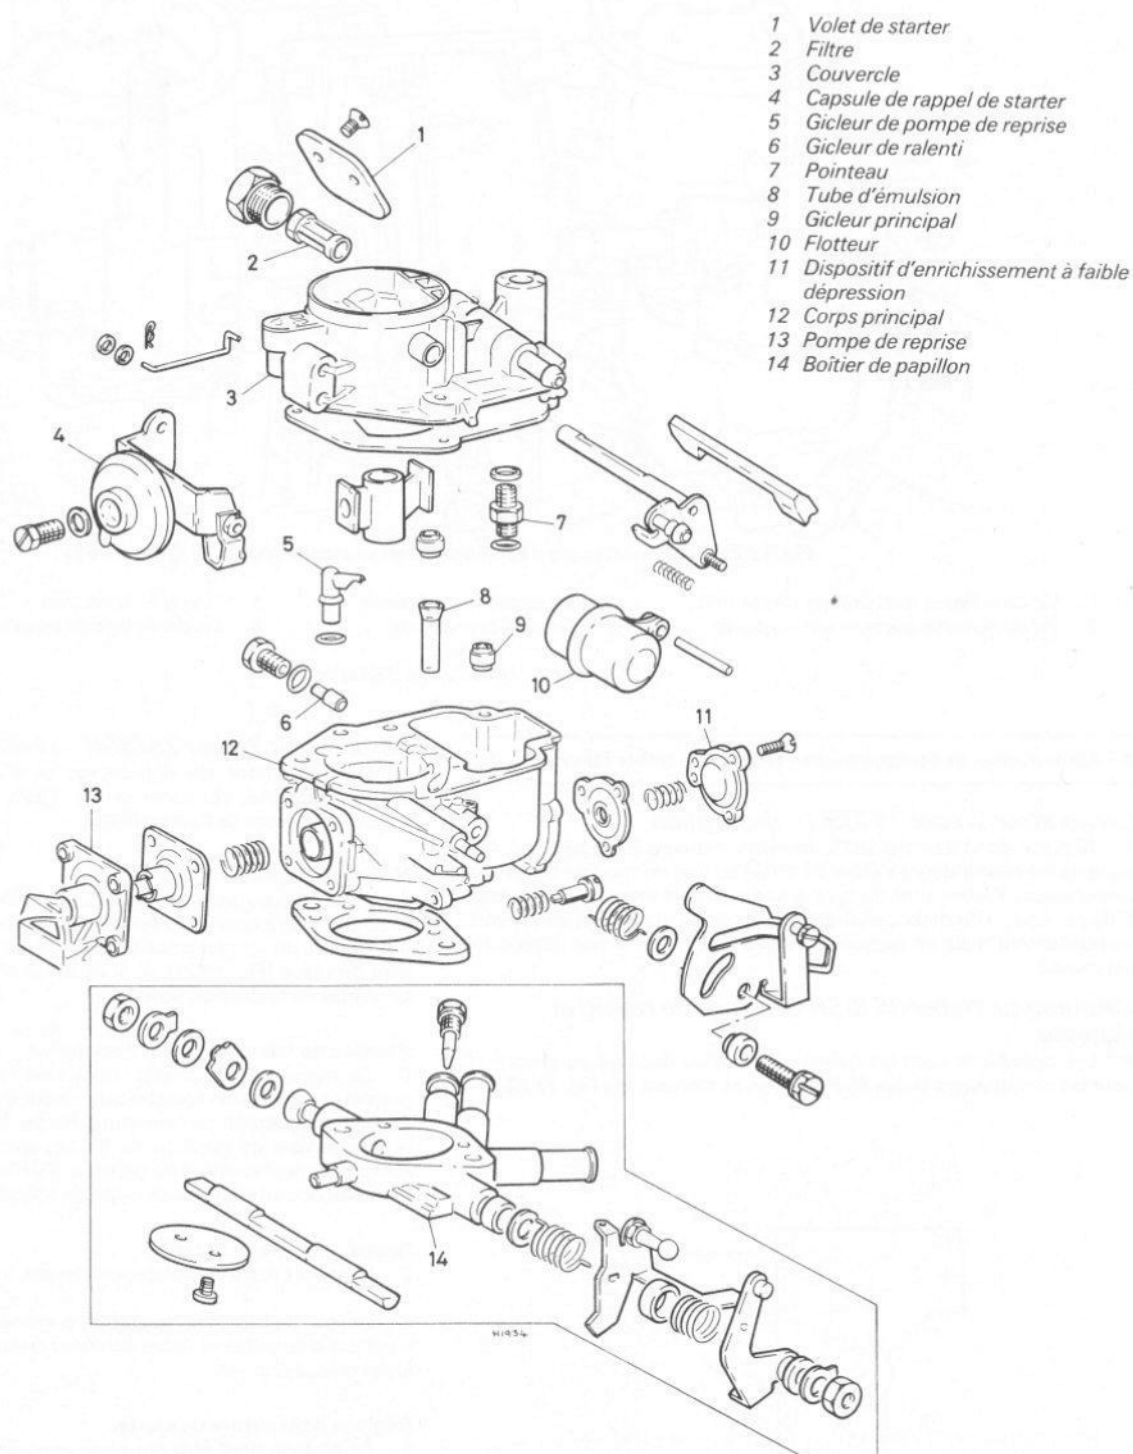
Eclaté du carburateur Weber 35 IBSH (Sec 8)
